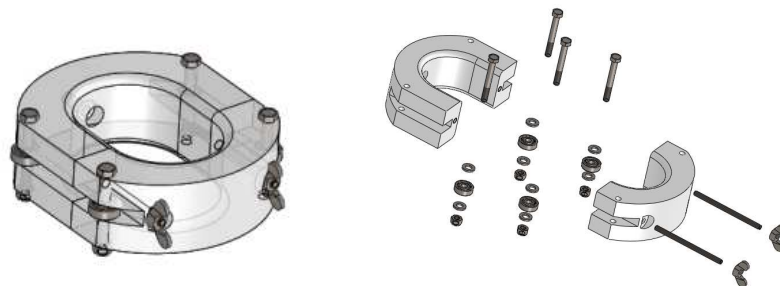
Conjunto da tornoeleira, nas vistas isométrica e explodida.
